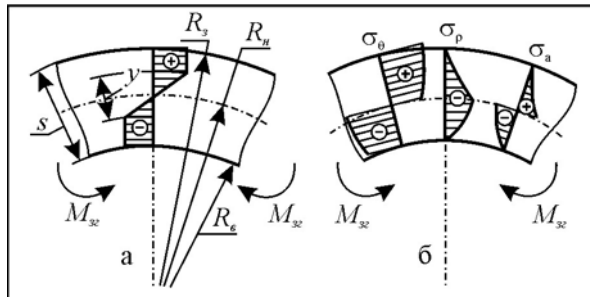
Епюри напружень за товщиною заготовки на стадіях: а – пружно-пластичної; б – пластичної
